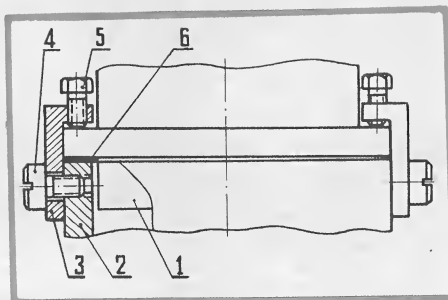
Крепление корпуса воздухоочистителя: 1 — нижняя часть воздухоочистителя; 2 — картер; 3 — прихват; 4 — винт М6; 5 — винт М4; 6 — прокладка.
